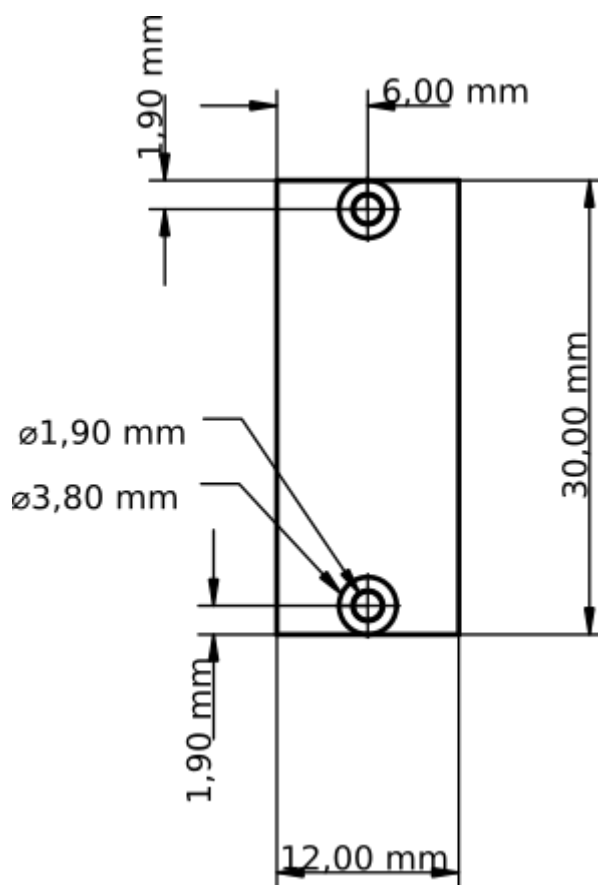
Držák motoru 1 (pohled zepředu)
